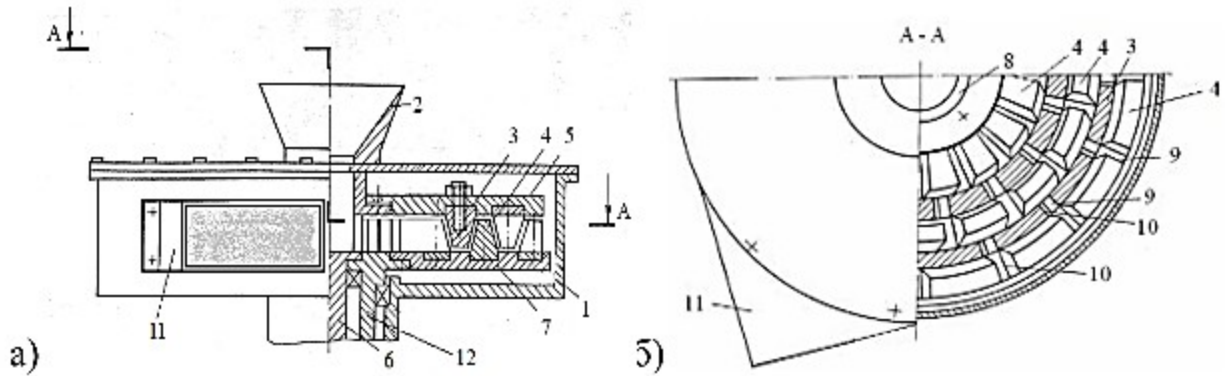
Схема відцентрово-роторного подрібнювача (а) та його ріжучих поверхонь (б): 1 – корпус; 2 – патрубок завантажувальний; 3, 4 – ріжучі елементи; 5 – диск-ротор верхній; 6 – вал внутрішній; 7 – диск-ротор нижній; 8 – вікна радіальні; 9 – канали (пази); 10 – стінка каналу; 11 - патрубок вивантажувальний; 12 – вал.
